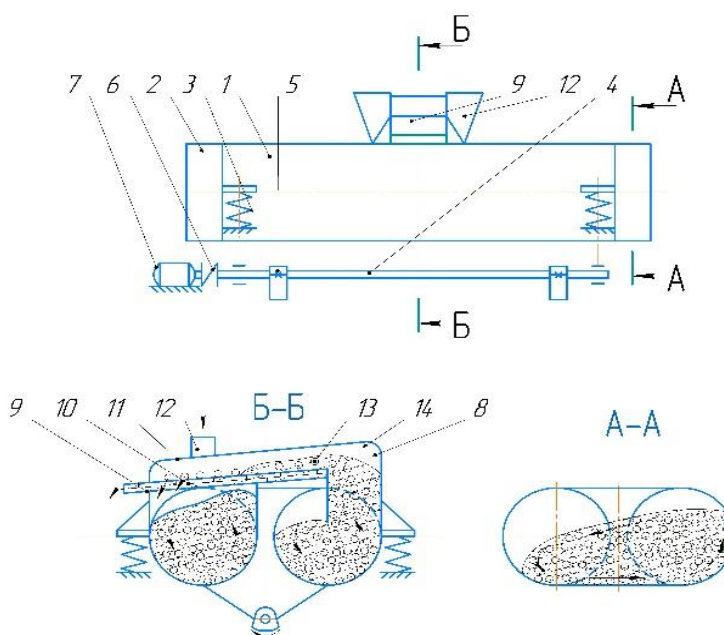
Конструктивна схема вібраційного млина: 1 – камера; 2 – перехідний жолоб; 3 – пружні елементи; 4 – вал вібророзбуджувача; 5 – дебаланси; 6 – еластична муфта; 7 – двигун; 8 – вертикальний жолоб; 9 – двоярусний лоток; 10 – решітка; 11 – отвори в боковій стінці лотка; 12 – завантаження; 13 – ударні тіла; 14 – матеріал.
